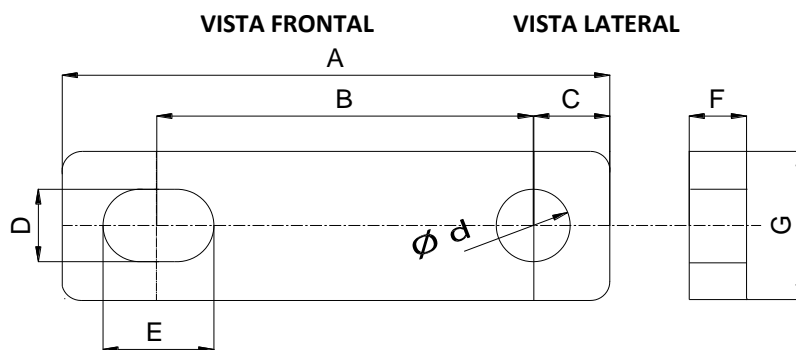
a: Herrajes para cruceta - Detalles de planchuela
